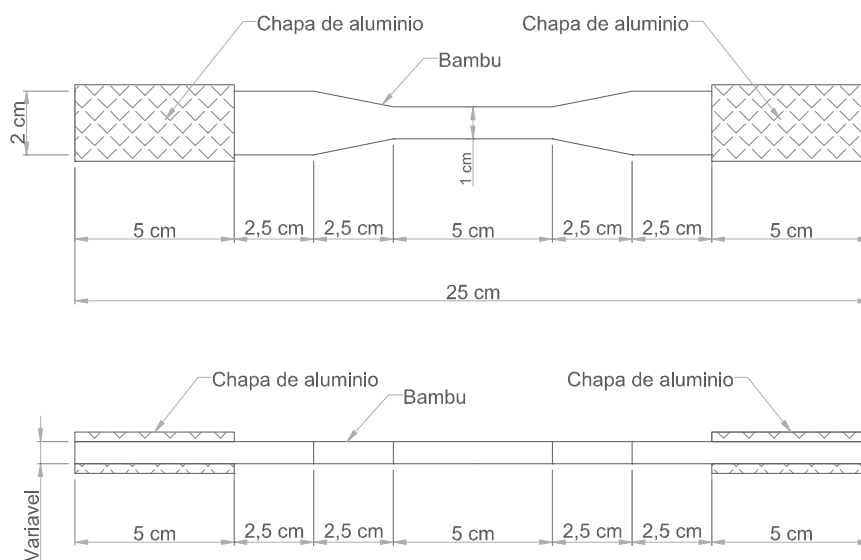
Geometria de corpos de prova para ensaio de tração
